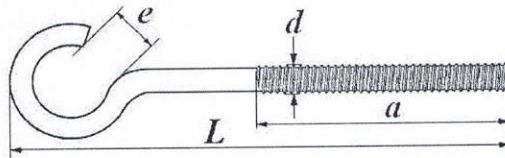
Конструкция и внешний вид винтов-полуколец
